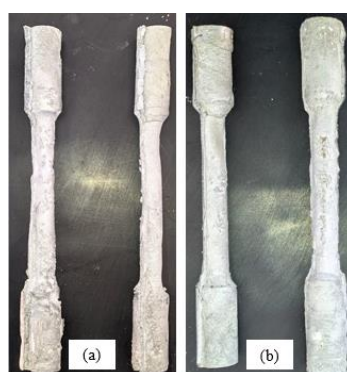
a) CP produzidos pelo molde com 100% de gesso b) CP produzidos pelo molde com 80% de gesso
